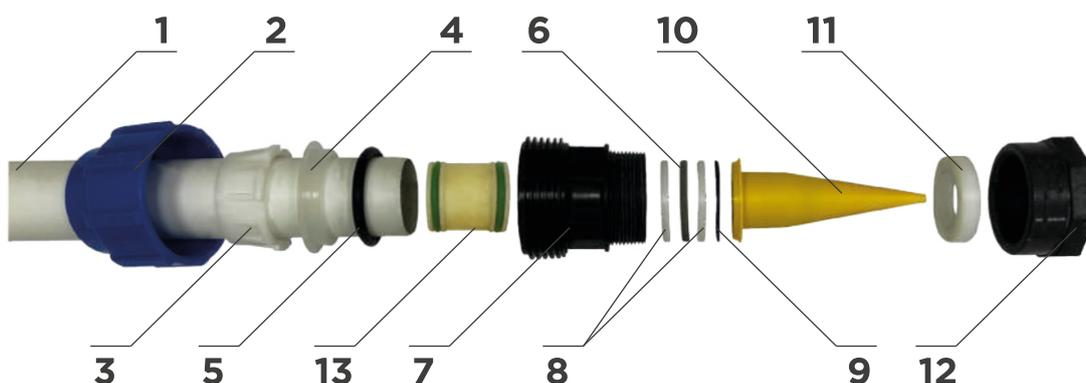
Схема разборки/сборки крышки и крепления насадки-носика
